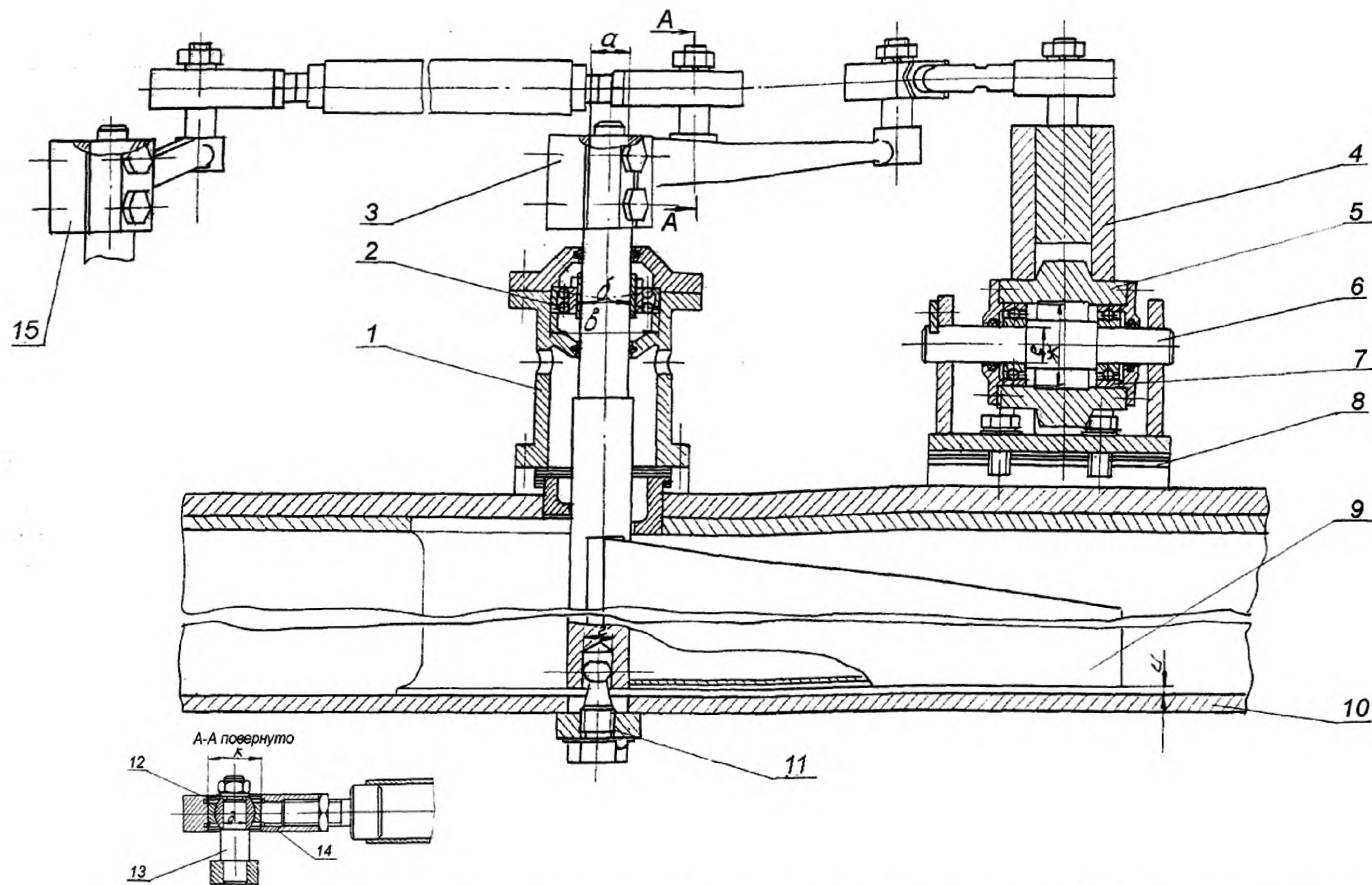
Схема центровки корпусов подшипников относительно вала
